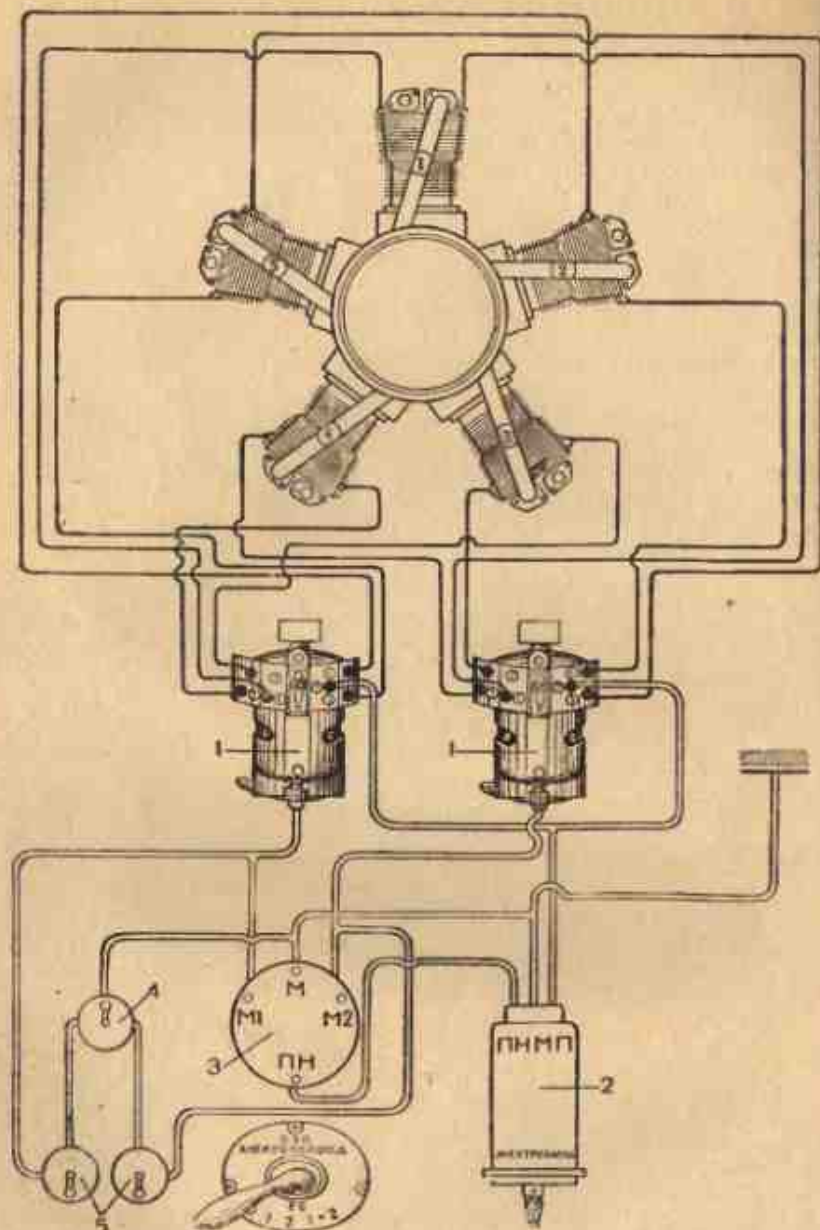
Схема внешней проводки зажигания на самолетах У-2, УТ-2, УТ-1 с переключателем ЕС.
